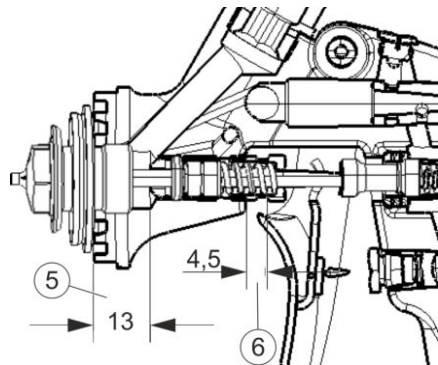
Dimensions du presse-étoupe d'aiguille
